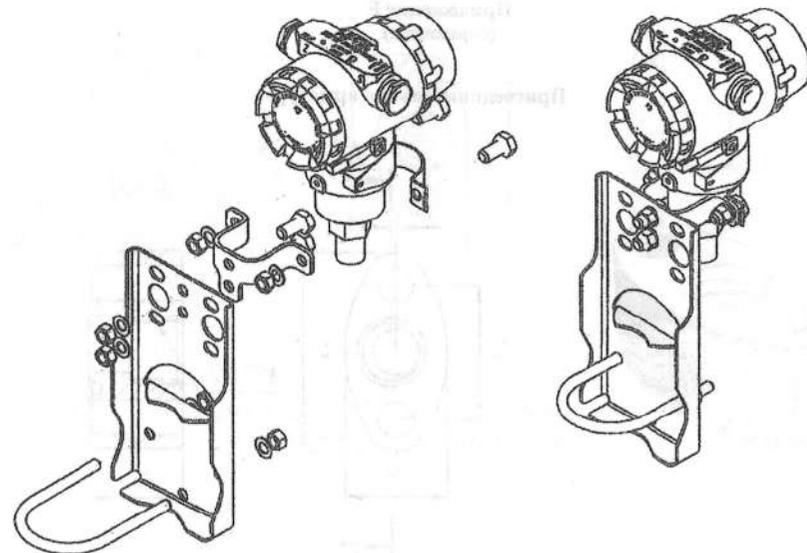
Монтаж датчика на плоский кронштейн, для крепления на трубе
